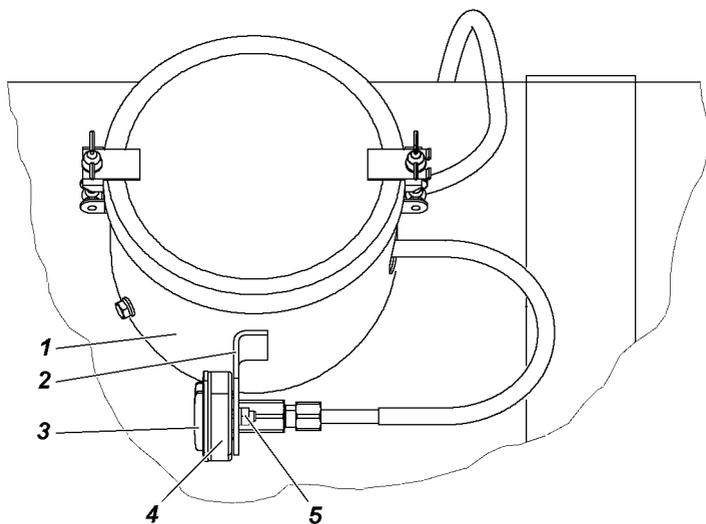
Установка заправочного устройства с продольным расположением баллона:
